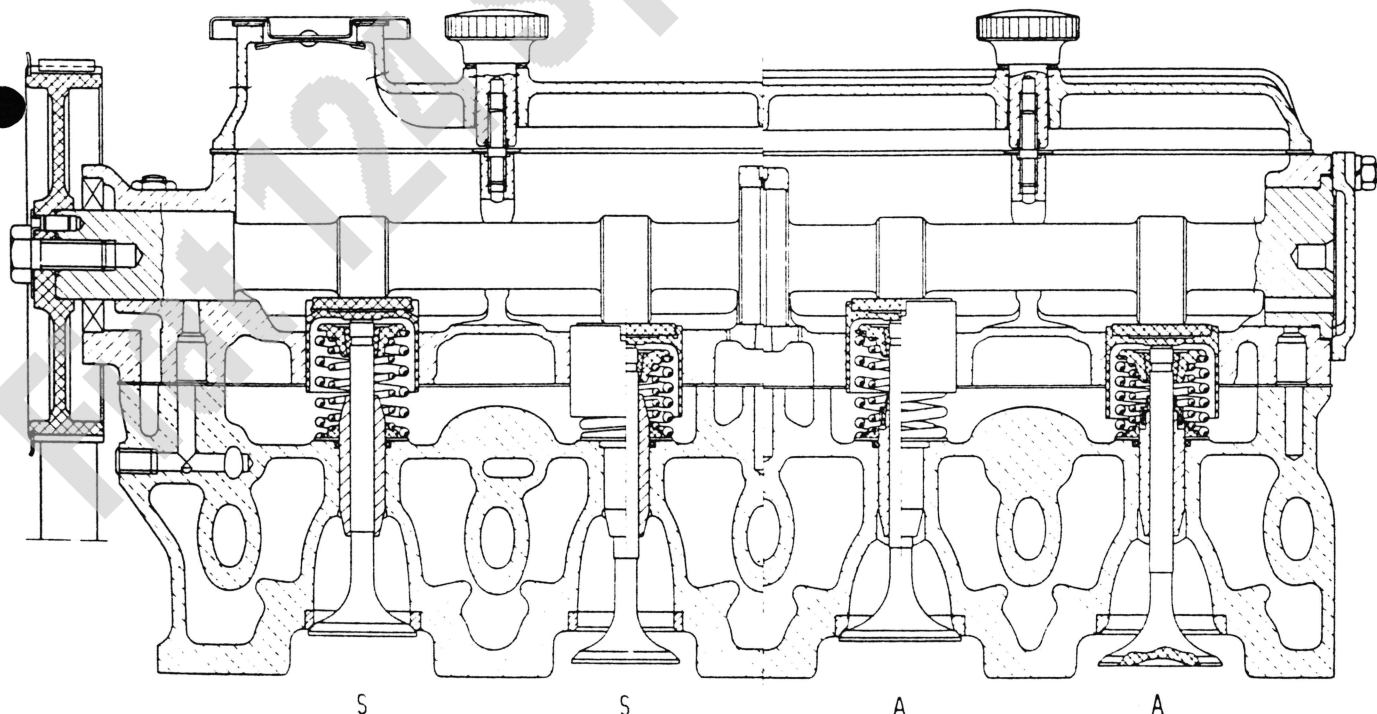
Längsschnitt durch den Zylinderkopf.
